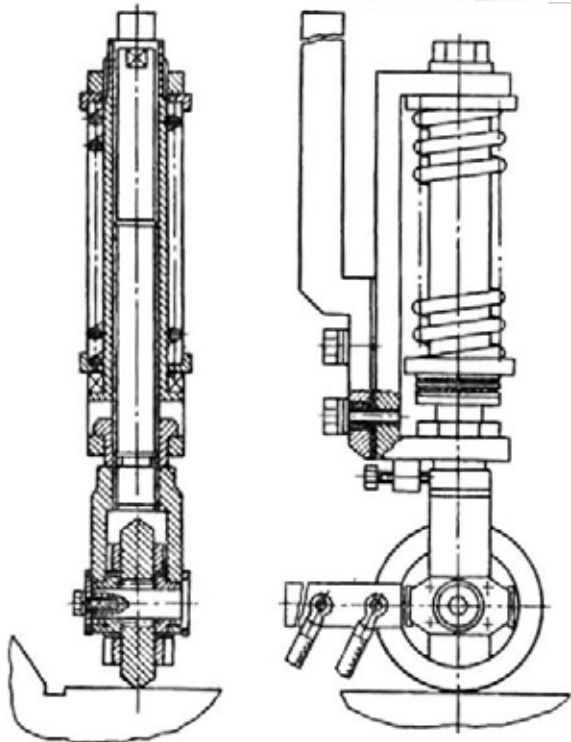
Роликовий пристрій для зміцнювального оброблення напрямних станини електромеханічним накатуванням
